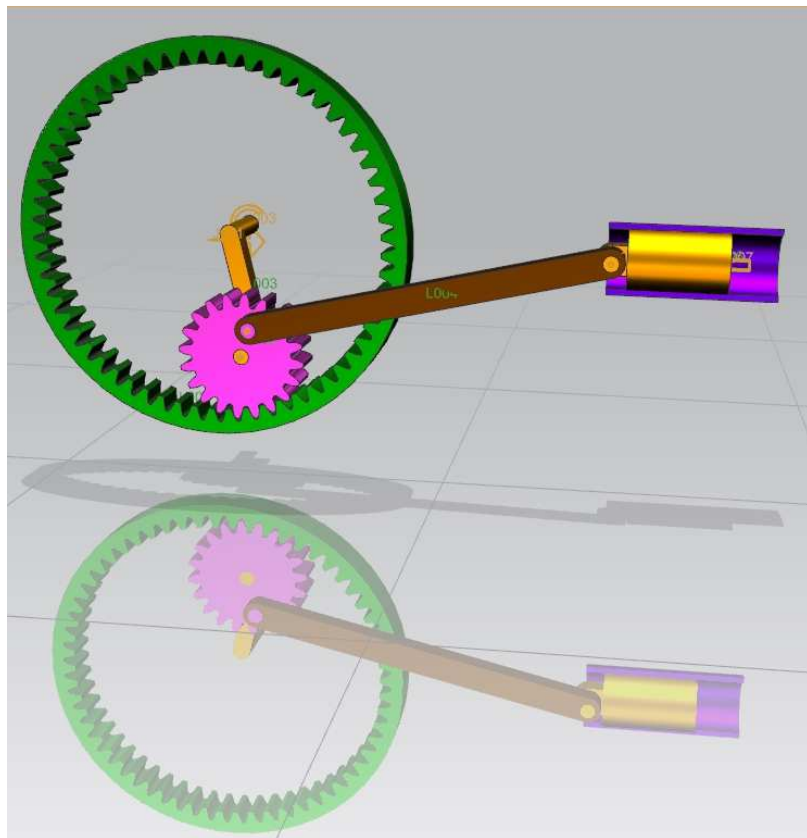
3D-модель планетарно-рычажного механизма
